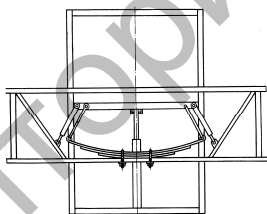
Схема маятниково-рессорной навески с амортизатором штанги опрыскивателя [38, 76]
